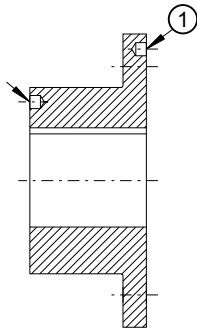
Position du trou d'équilibrage pour l'équilibrage à deux plans
